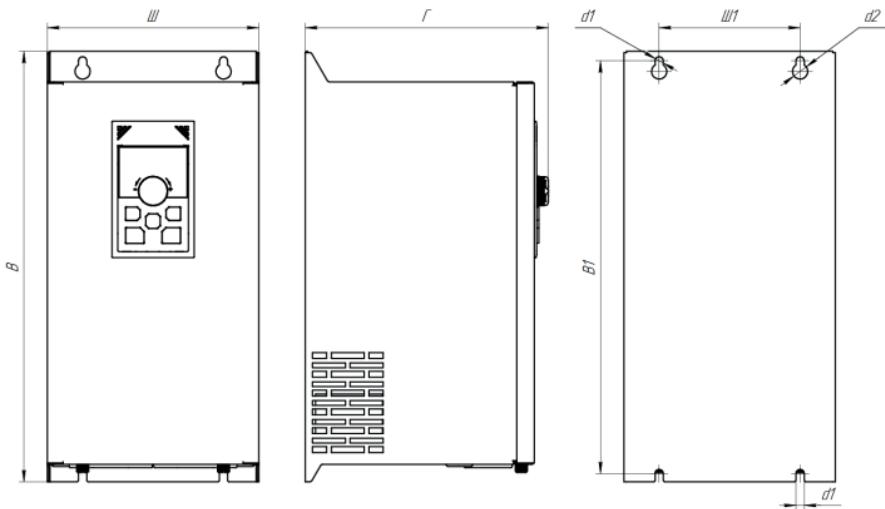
Установочные и габаритные размеры тормозного модуля BU, типоразмер 2
